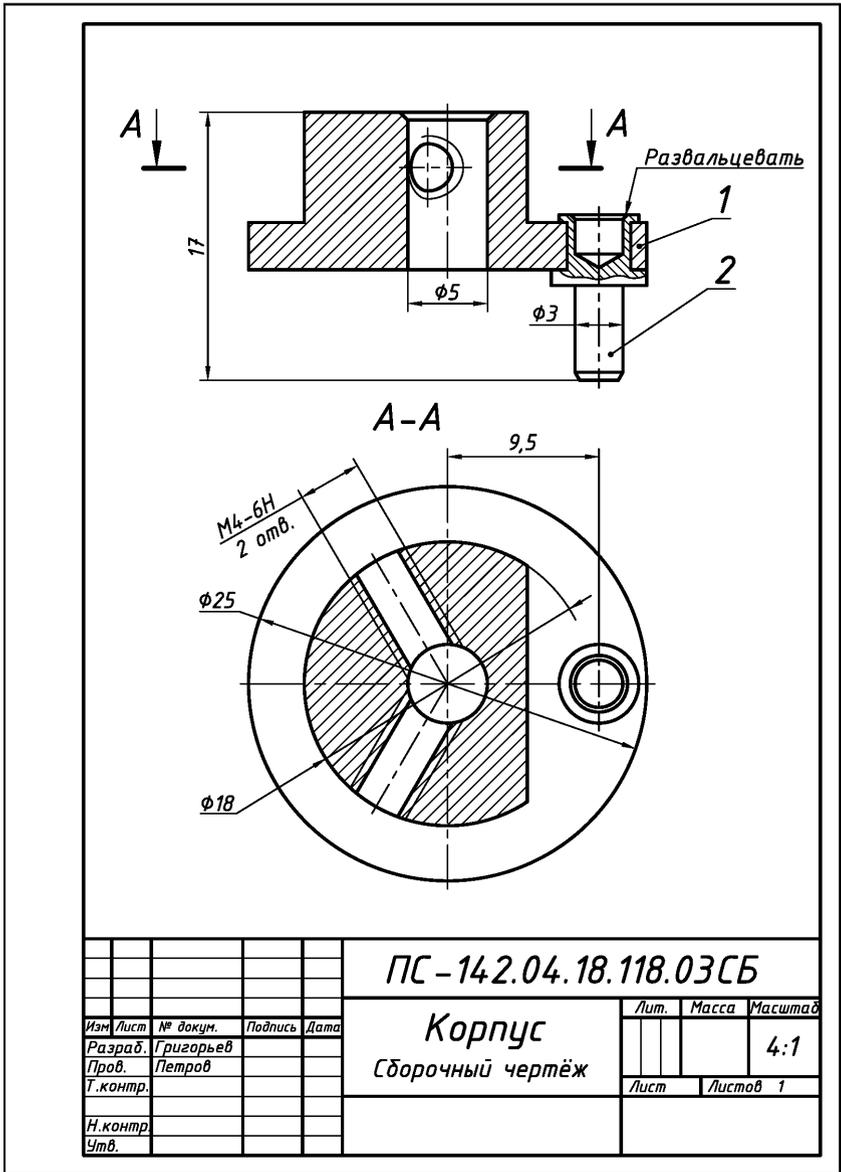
Оформление рабочего чертежа сборочной единицы «Корпус», образованной развальцовкой
